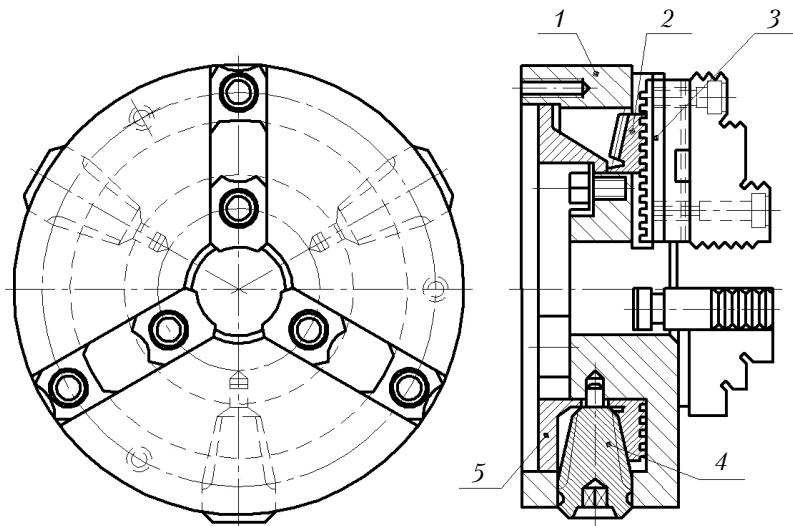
Схема токарного спирально-реечного самоцентрирующего патрона
